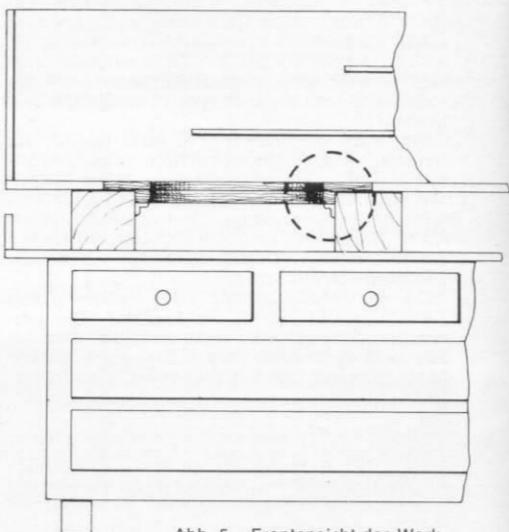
Frontansicht des Werkisches mit der Vorsteckplatte, deren Befestigung (Kreis) in Abb. 6 nochmals verdeutlicht wird.
